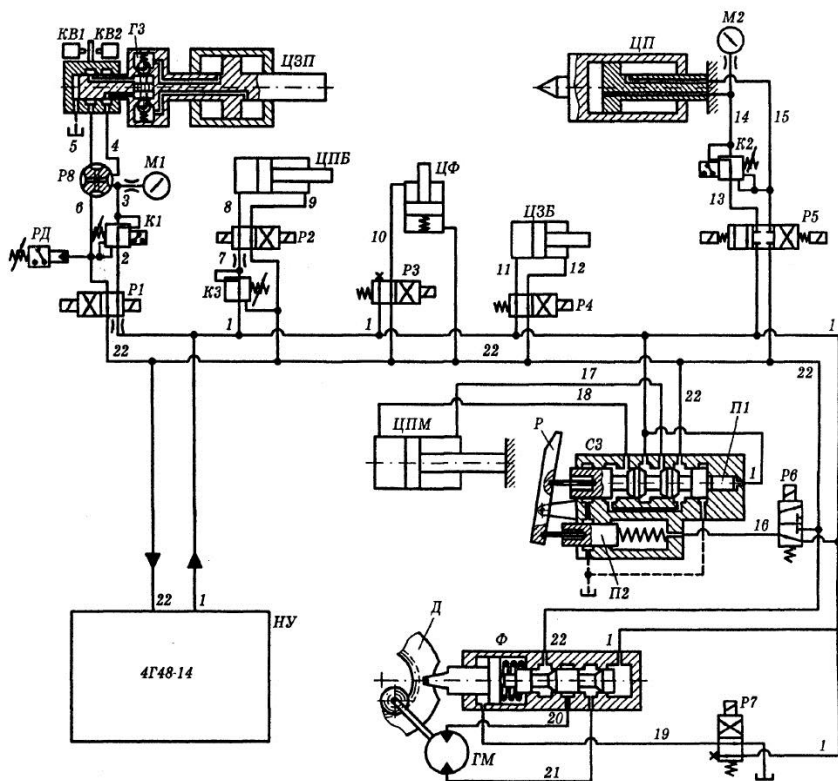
Токарный патронно-центровой полуавтомат с ЧПУ 1725МФЗ
